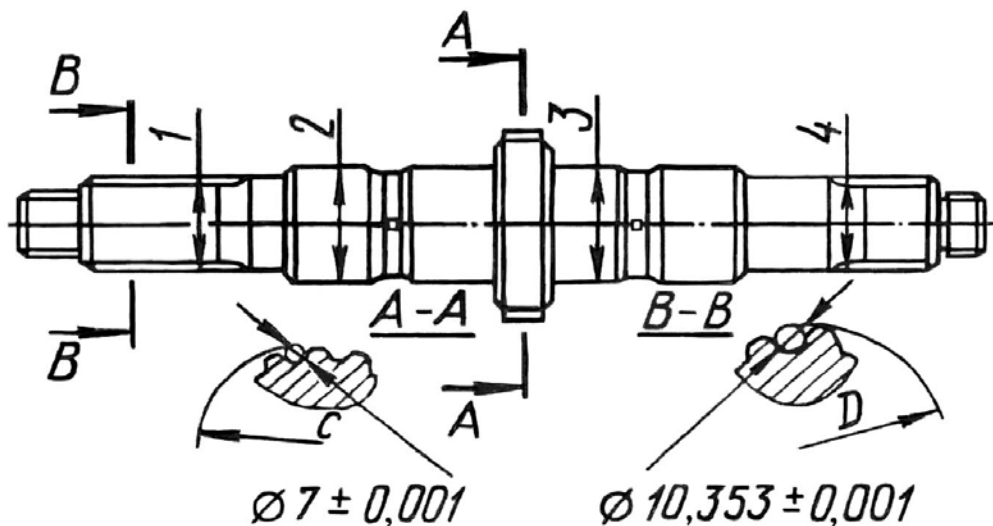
Расположение шеек первичного вала раздаточной коробки:
